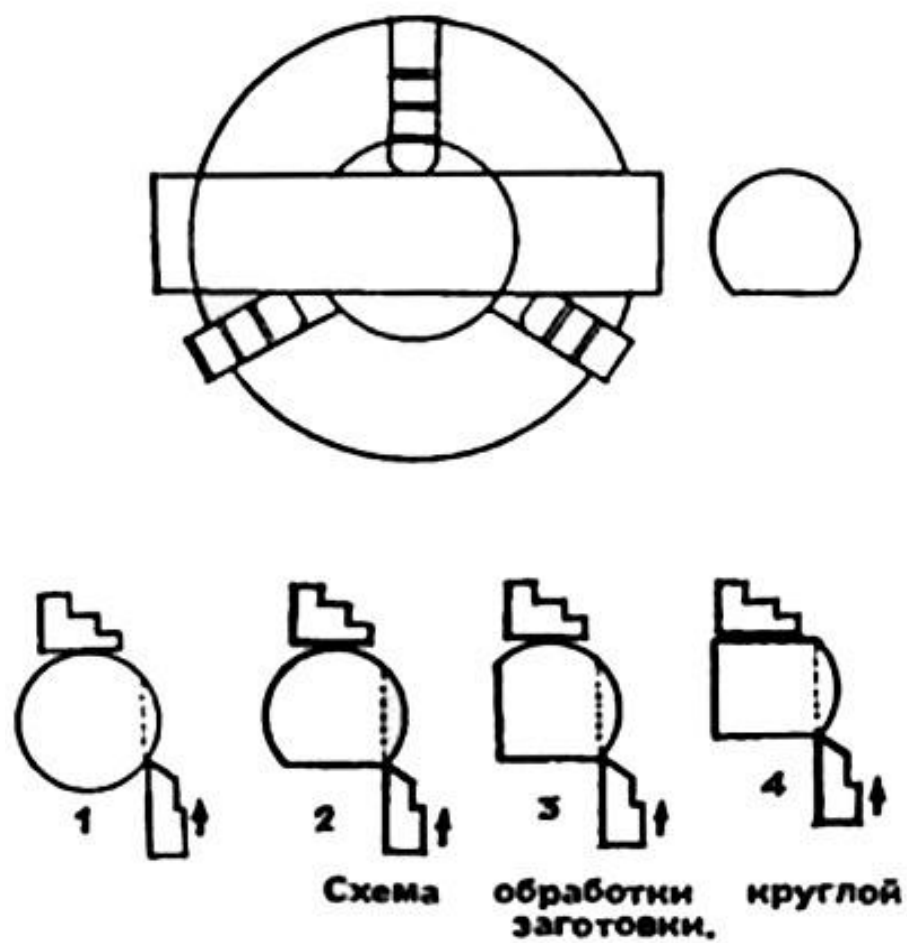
Общий вид закрепления заготовки в трех кулачковый патрон
